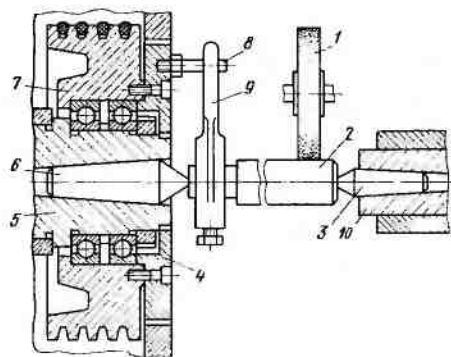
Установка заготовки в неподвижных центрах круглошлифовального станка
